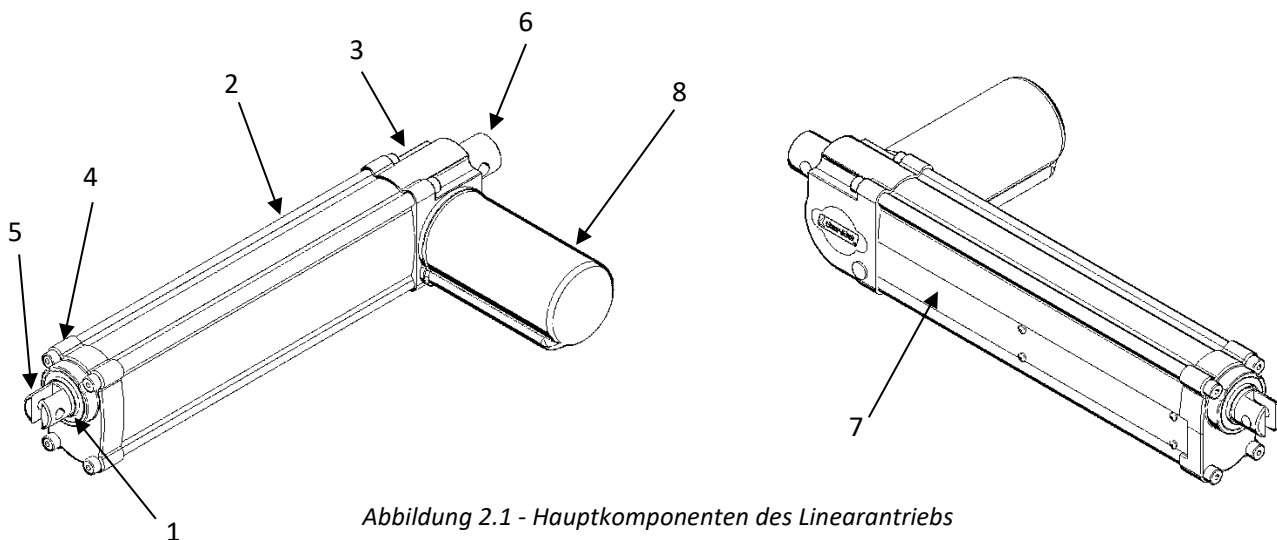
Hauptkomponenten des Linearantriebs
